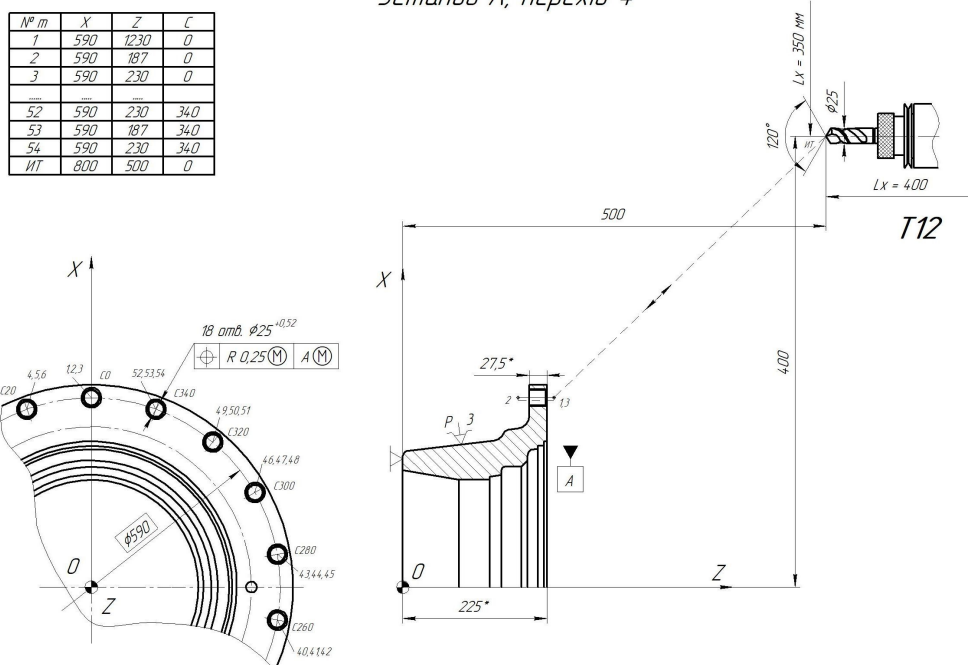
Установ А, перехід 4: схема обробки деталі та координатне розташування інструмента
